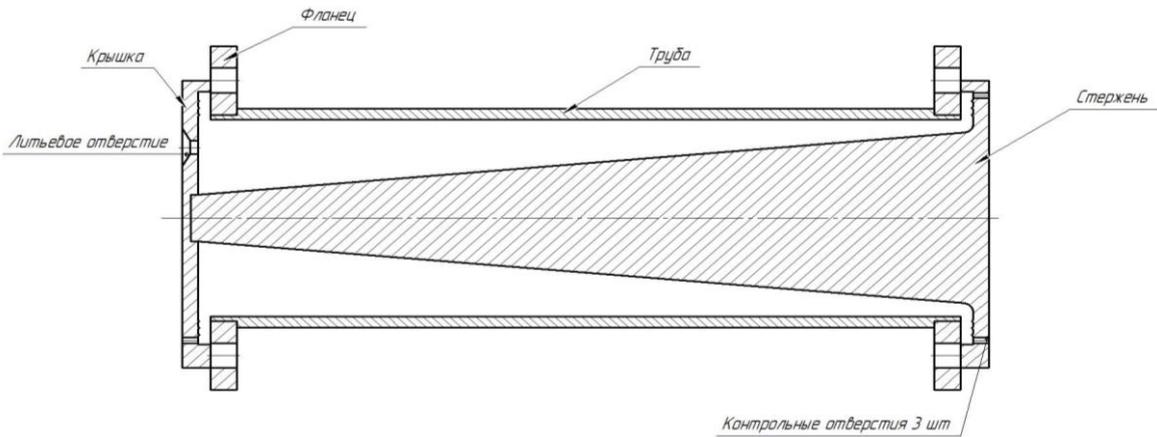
Схема сборки пресс-формы второй половины корпуса эжектора
